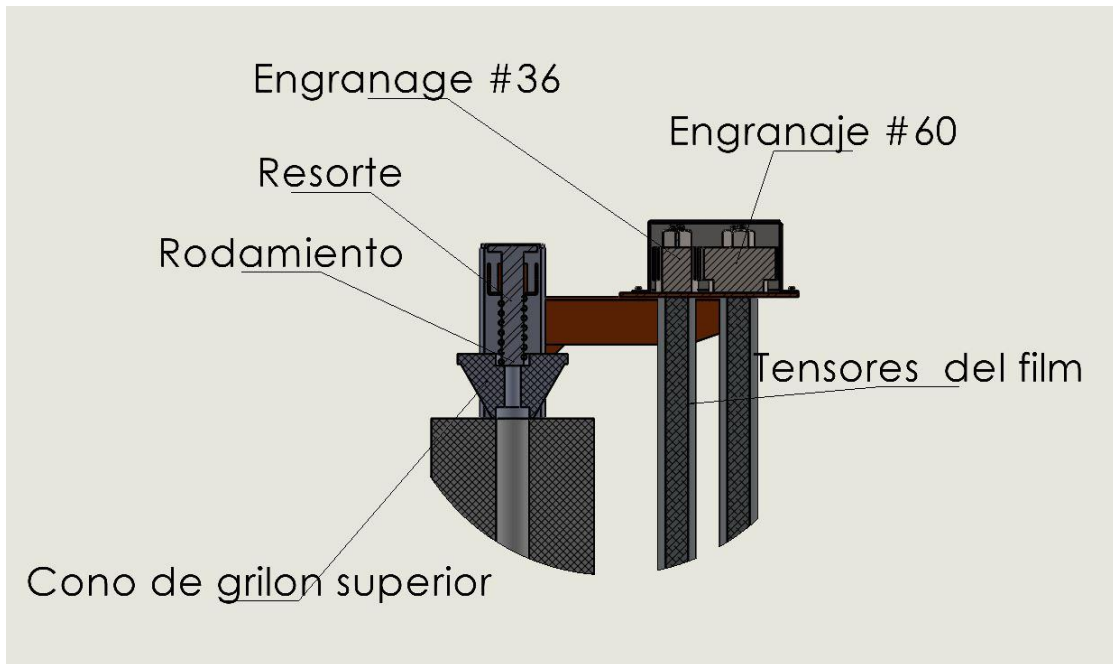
Detalle del conjunto de rodamientos superior y engranajes tensores.
